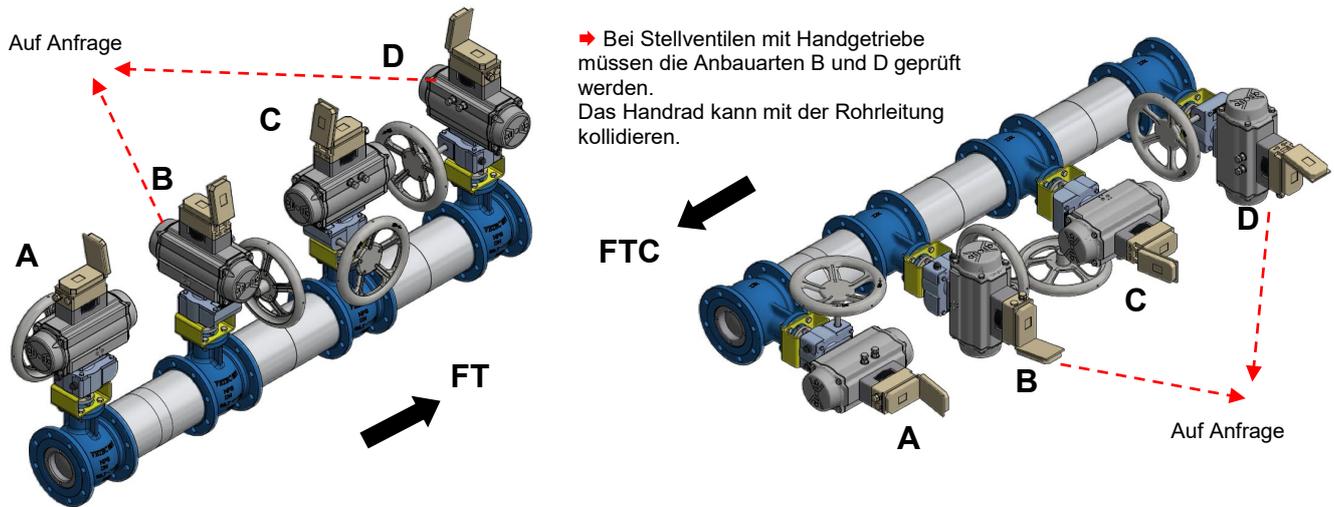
Stellventil Typ 62.7/AT-HG • horizontale Einbaulage • Anbauarten des Antriebs auf den Ventil A, B, C, D
